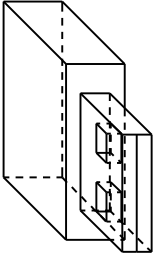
držák zásuvky na tažné zařízení v technické dimetrii
